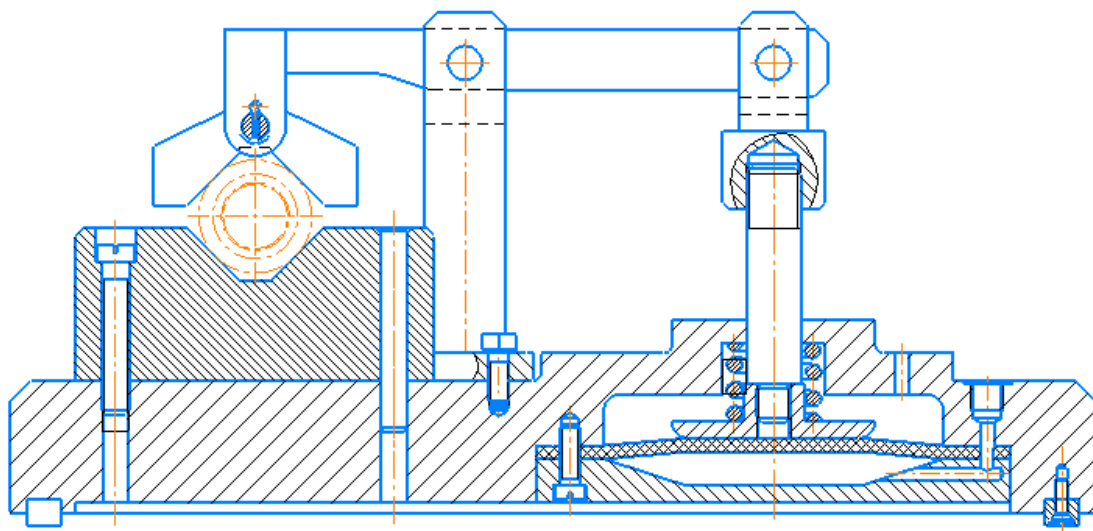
Компоновка (общий вид) приспособления показан на чертеже
